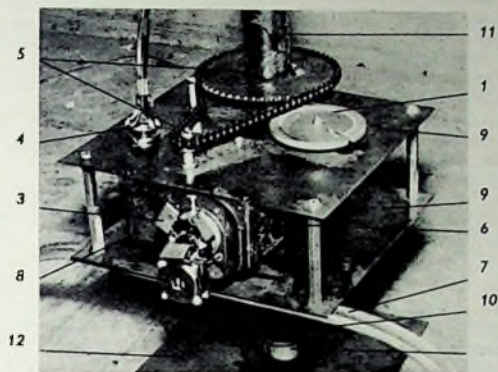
Antriebsaggregat des Antennenmastes; 1 Seilscheibe mit Richtungsgeberpotentiometer, 2 Endverschraubung mit Senkung, 3 Motor mit Entstörung, 4 Steckverbindung für Stromzuführung und Steuerleitung, 5 Kettenräder mit Kette, 6 Sicherung für Motor, 7 Halterung für das Antriebsaggregat, 8 Getriebe am Motor, 9 Montageplatten, 10 Mast, 11 Rohrstützen (wird nach dem Zusammenbau des Getriebes über den Mast geschoben), 12 Grundplatte mit Senkung als Gegenlager
